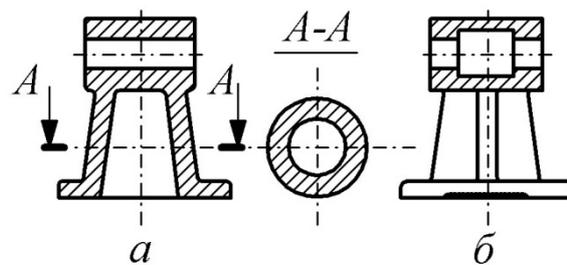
Ескіз деталі: *a* – перший варіант конструкції;
